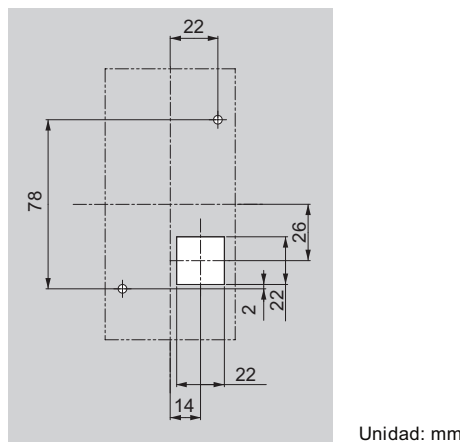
Dimensiones de corte del panel (instalación con montaje externo/frontal)
